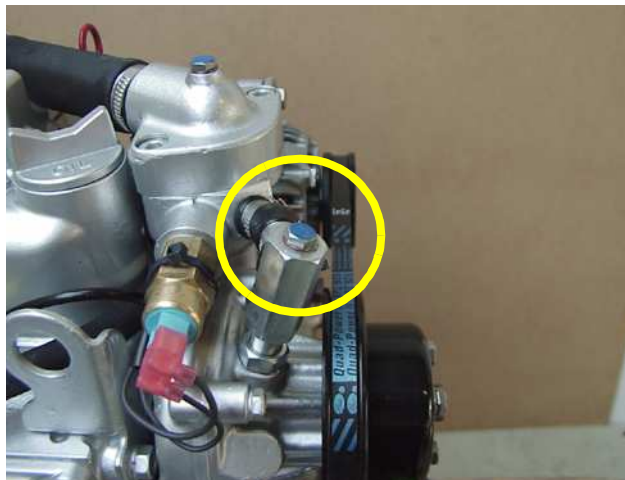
Entlüftungsschraube interne Kühlwasserpumpe
